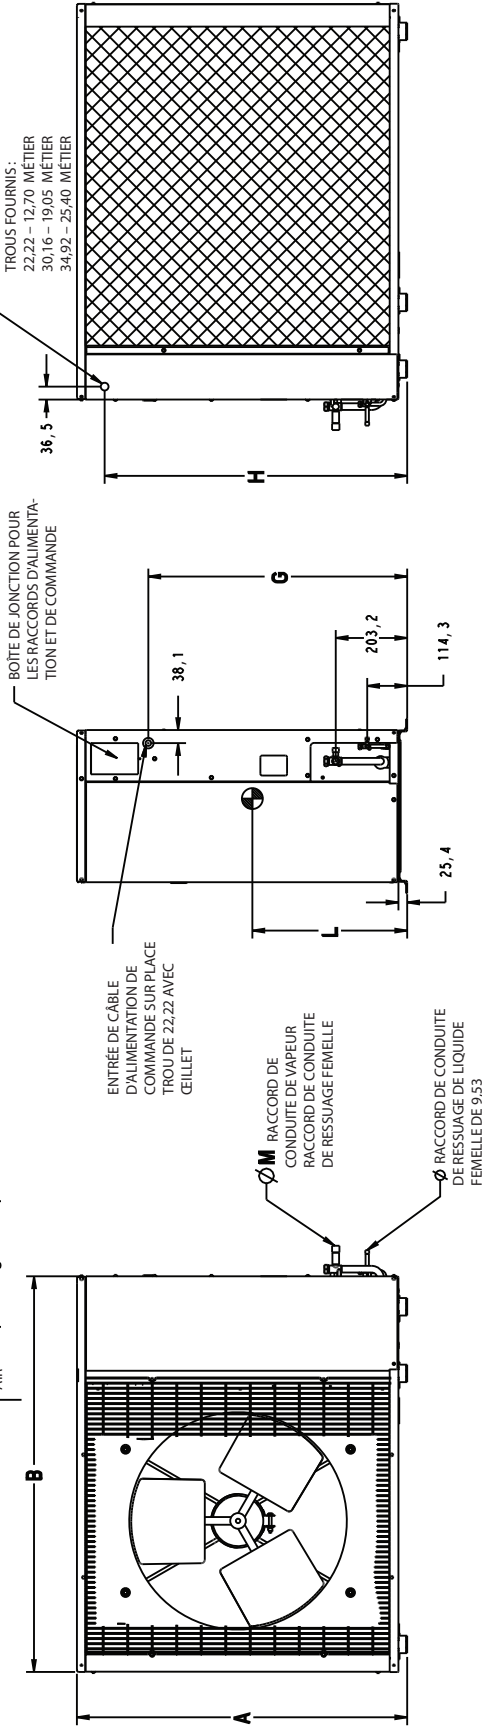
Dimensions de l'appareil extérieur 38HDR – SI
